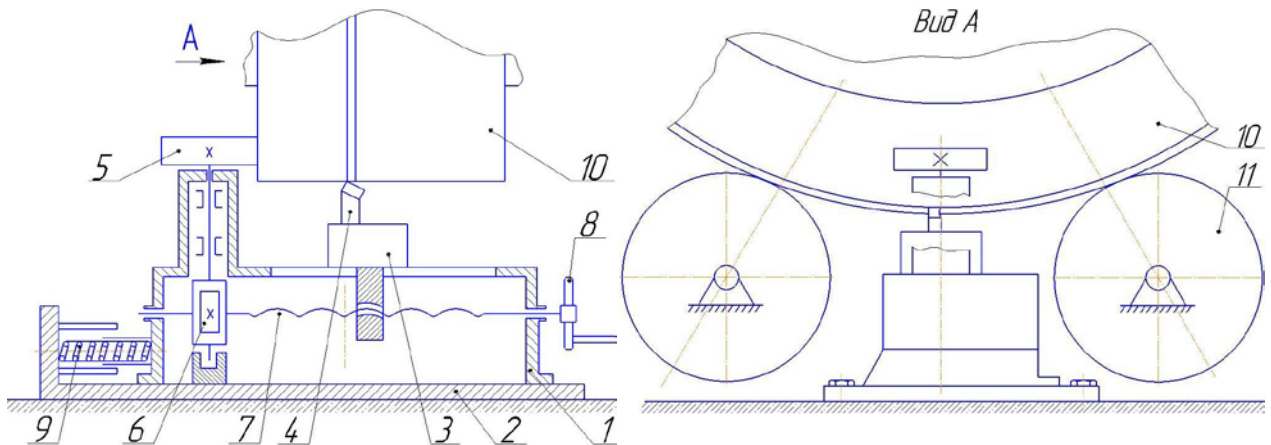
Устройство фирмы Союзремонт (СССР) для проточки бандажей и роликов вращающейся печи: 1 - основание станка; 2 - станина; 3 - суппорт; 4 - резец; 5 - ролик; 6 - червячное колесо; 7 - ходовой винт; 8 - рукоятка; 9 - пружина; 10 - бандаж; 11 - опорный ролик
